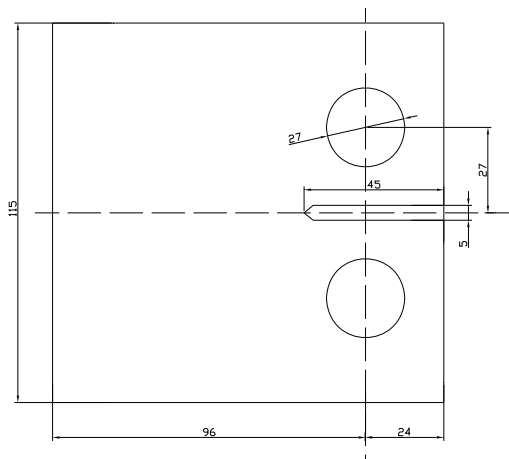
Dimensiones de la probeta CT (B = 11.2 mm)
